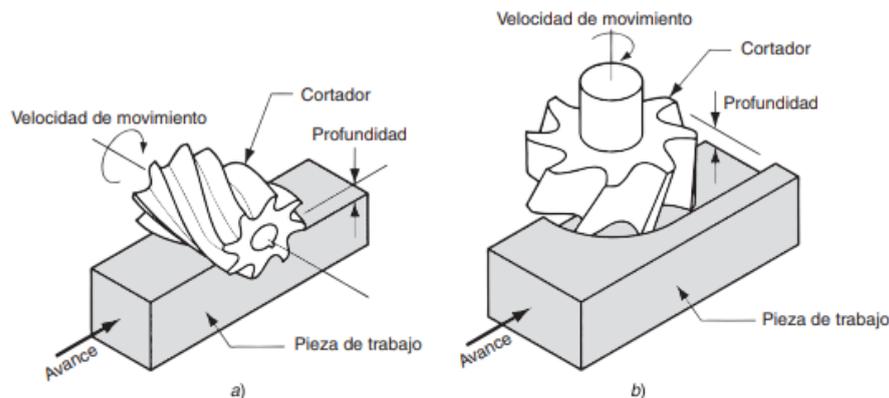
Operación de fresado: a) Fresado periférico y b) Fresado Frontal
